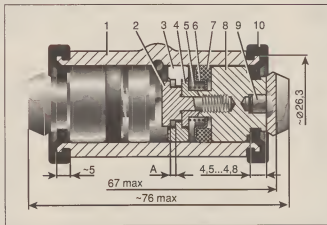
Тормозной цилиндр заднего колеса: 1 – цилиндр; 2 – упорный винт; 3 – упорное разрезное кольцо; 4 – сухарь; 5 – пружина; 6 – опорная чашка; 7 – резиновое кольцо; 8 – поршень; 9 – упорная пружина; 10 – защитный резиновый колпачок.
